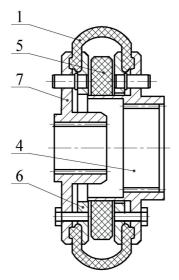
Муфта шинно-зубчатая: 1 – высокоэластичная оболочка; 4 – зубчатая полумуфта; 5 – прокладка; 6 – полукольцо; 7 – полумуфта
